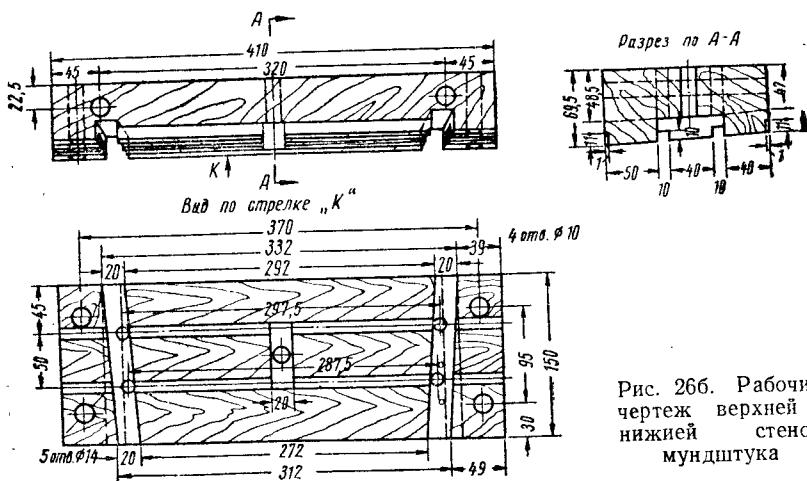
Рабочий чертеж верхней и нижней стенок мундштука
